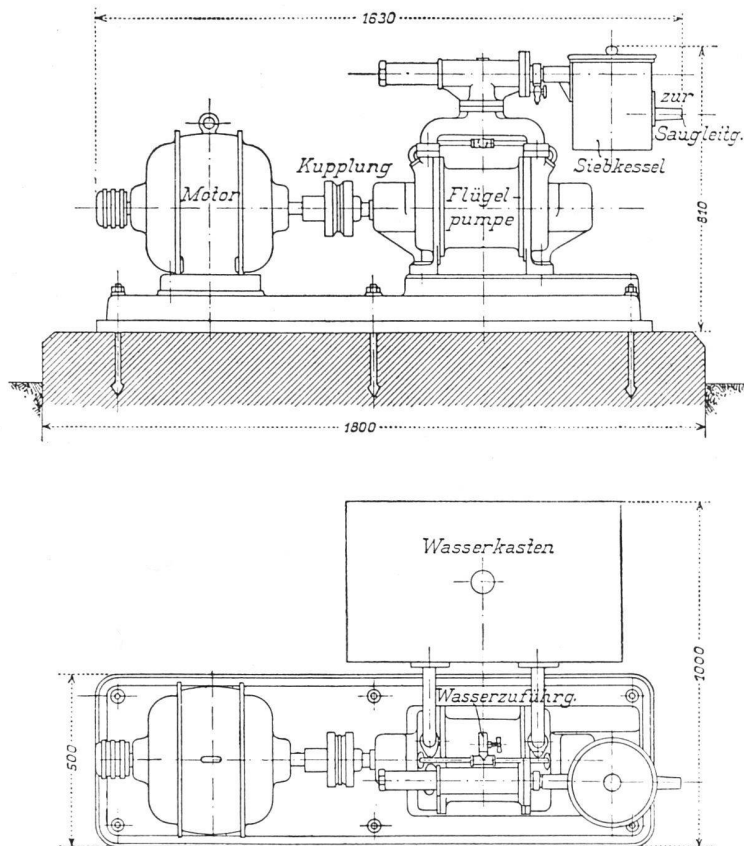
Entsaugungs-pumpe — Ansicht und Grundriß — Maßstab 1:20
